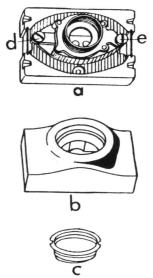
Base portafusible de cartucho Diazed, de la firma Siemens. a) Zócalo. b) Tapa. c) Casquillo roscado. d) Tornillo de conexión a la pieza de contacto, con el tornillo de ajuste. e) Tornillo de conexión al casquillo roscado.
